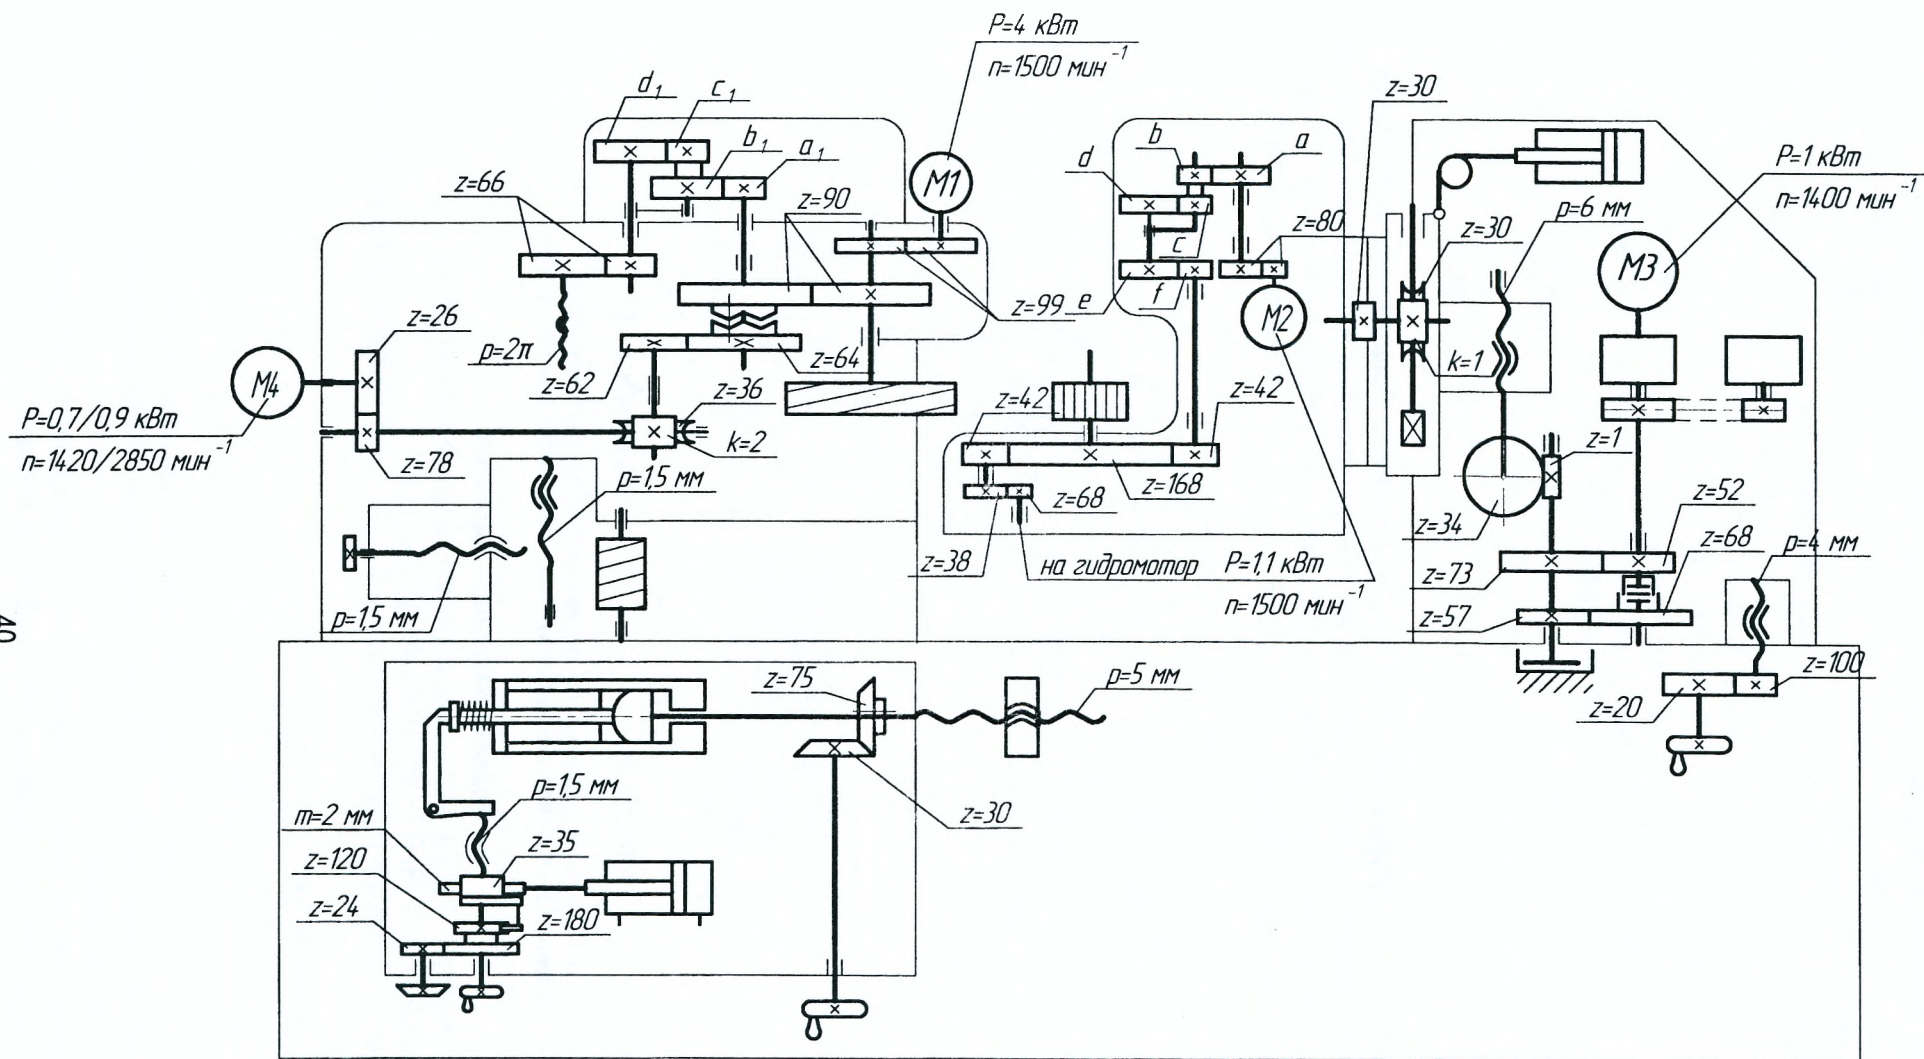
Кинематическая схема зубошлифовального станка мод.5B833
